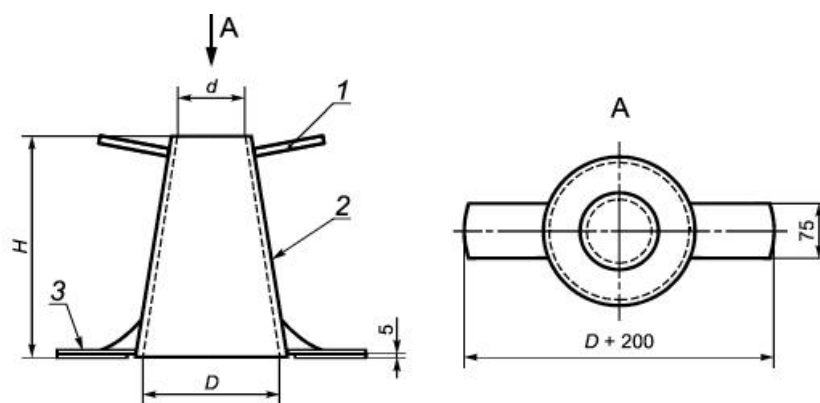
Конус для определения подвижности: 1 – ручка; 2 – корпус; 3 – упоры
